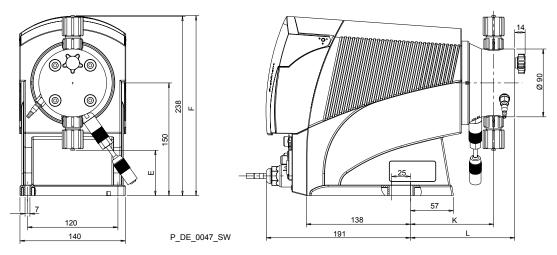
Hoja de dimensiones del tipo delta® con válvula de aireación, versión de material NP; dimensiones en mm
